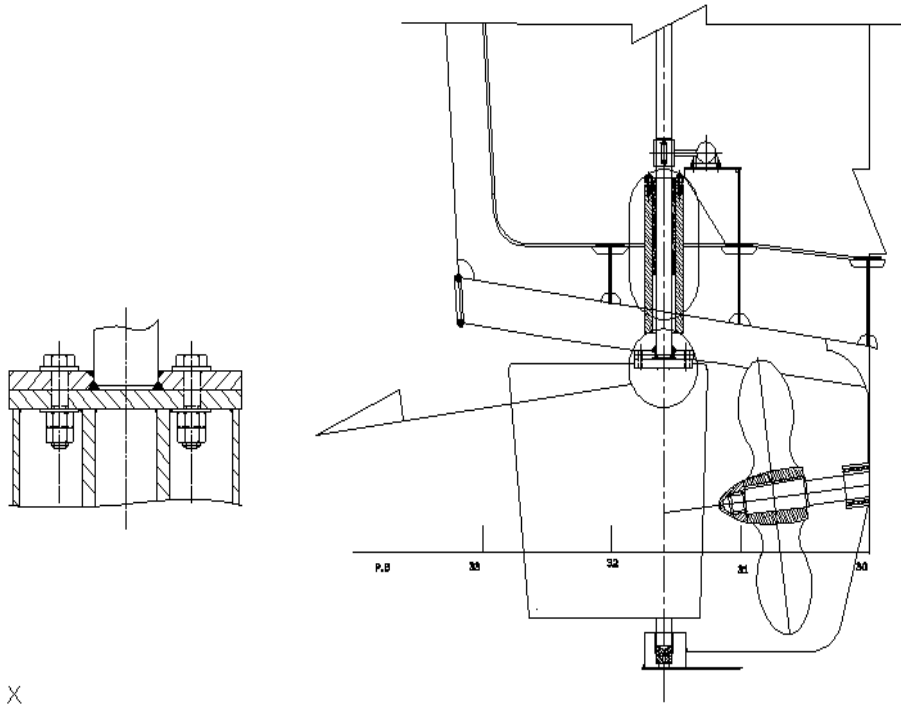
Coupe transversal (A) et longitudinale (B) d'un safran.
